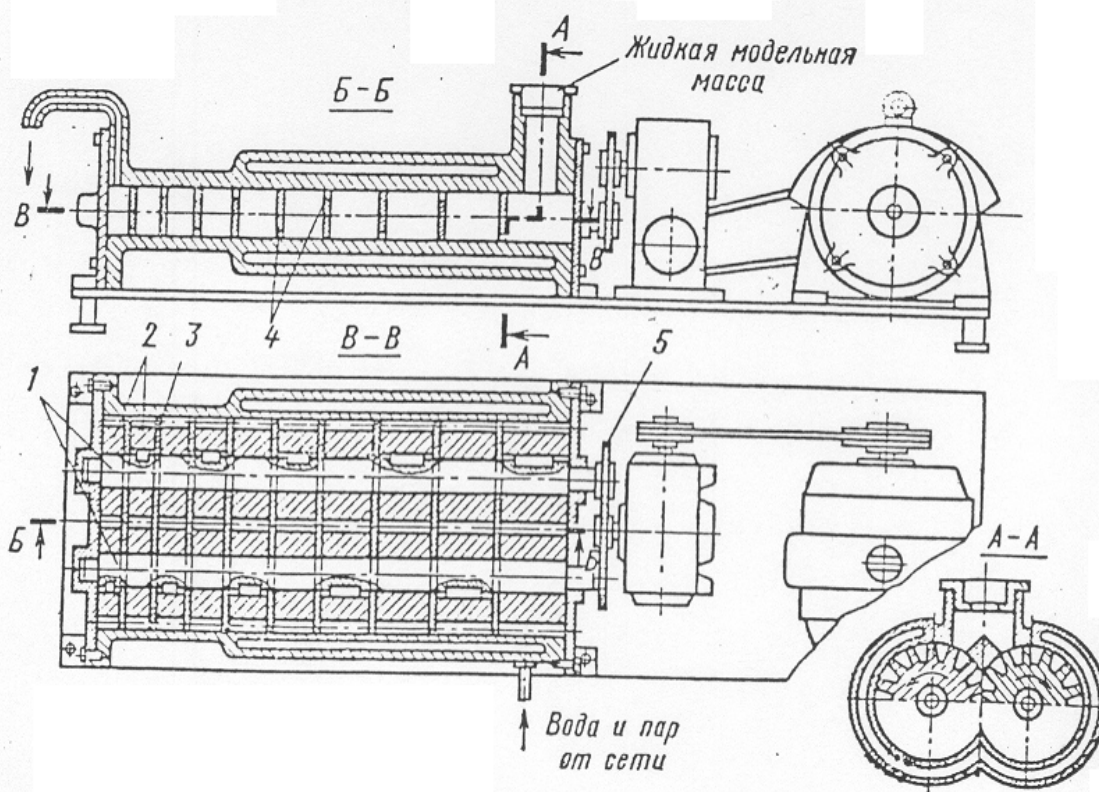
Схема шестеренного смесителя для приготовления пастообразного модельного состава с воздухом: 1 – валы; 2 – шестерни; 3 – перегородки; 4 – выпускное отверстие; 5 – привод смесителя.
